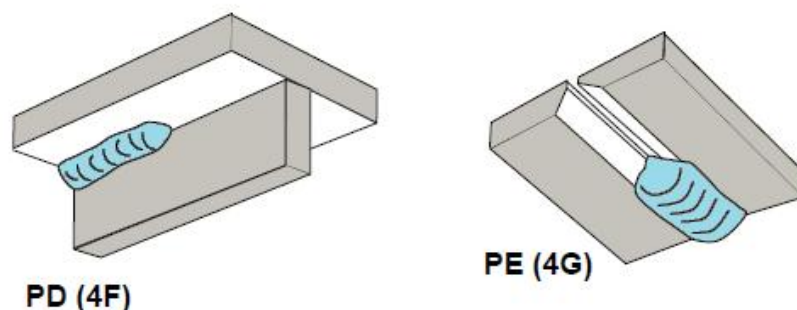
Posições de soldadura ao teto do tipo PD e PE
